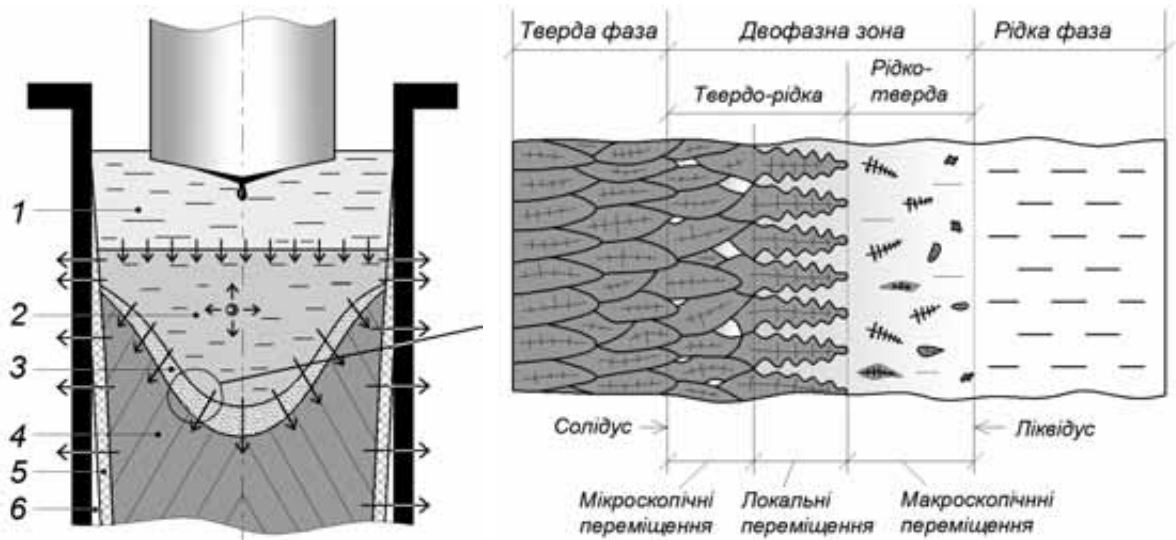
Схема кристалізації зливка ЕШП і структура двофазної зони (стрілками позначений напрямок теплового потоку): 1 – шлакова ванна; 2 – металева ванна; 3 – двофазна зона; 4 – твердий метал (зливоч); 5 – шлаковий гарнісаж; 6 – усадковий зазор
